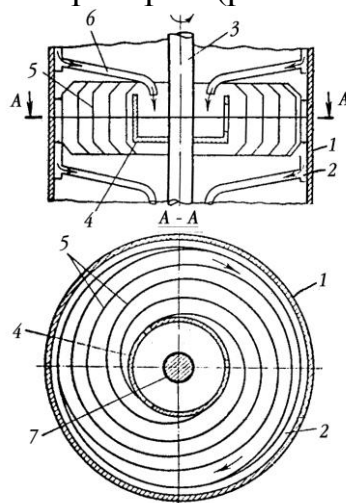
Ректификатор со спиралеобразным ротором: 1 – корпус; 2 – кольцевой карман; 3 – вал; 4 – перфорированный стакан; 5 – спиральная лента; 6 – лоток; 7 – вал
